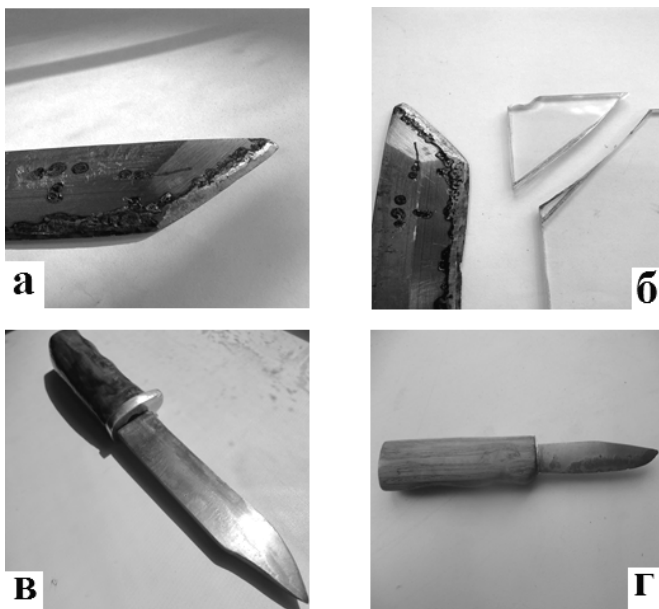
Титановые клинки с обработанной режущей кромкой (а, б), ножи из титанового сплава ВТ1-0 с композитной режущей кромкой (в, г)
